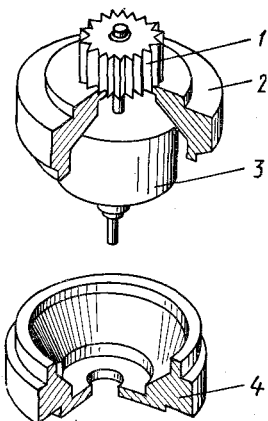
Ротор шагового двигателя с выносной катушкой:
